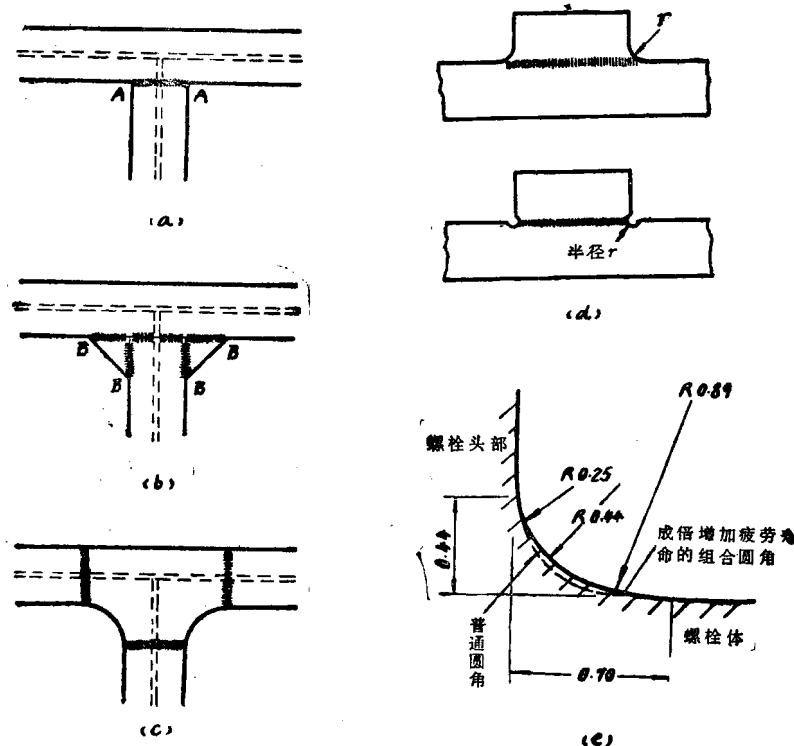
8 焊接结构及零件截面几何形状的改进
